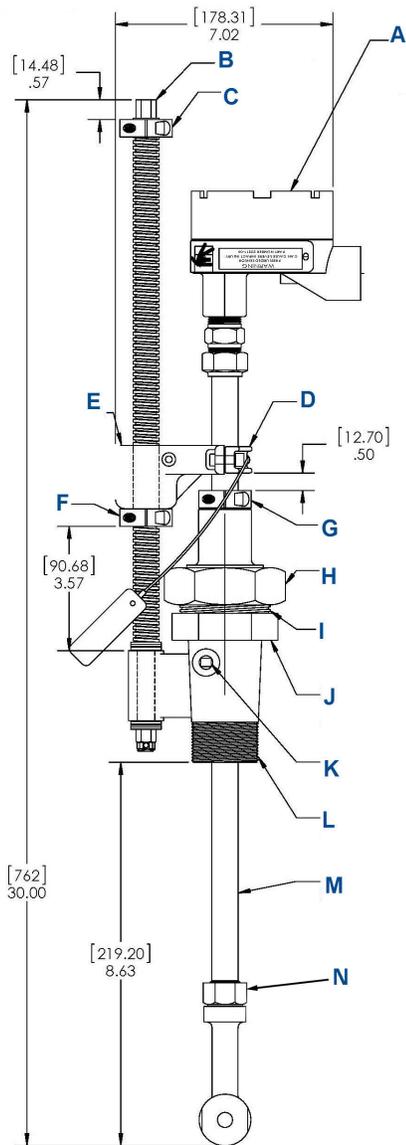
Desenho dimensional do conjunto de retração manual PN 2311-01
